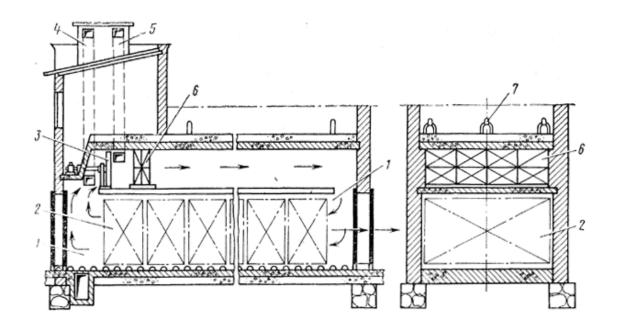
Схема туннельной сушильной установки: 1 – сушильная камера; 2 – штабель; 3 – вентилятор с электродвигателем; 4 и 5 – приточный и вытяжной каналы; 6 – пластинчатый калорифер; 7 – психрометр.
